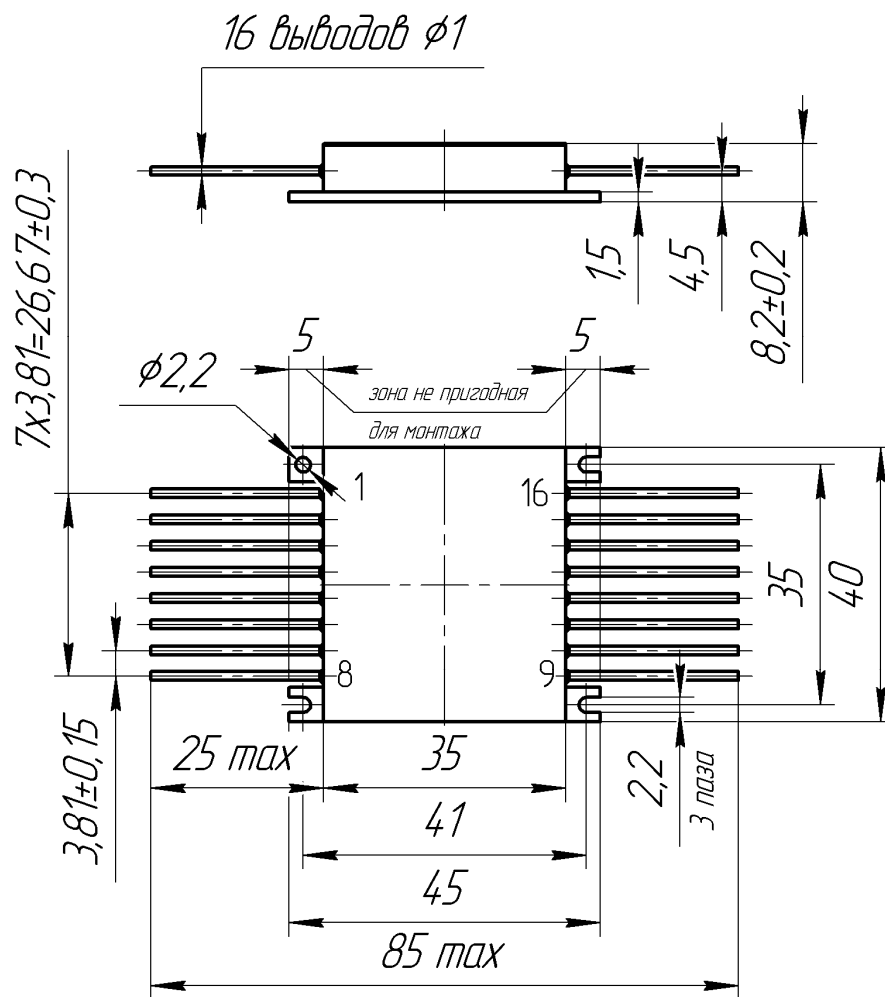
Габаритный чертеж микросборки 2626KB014
